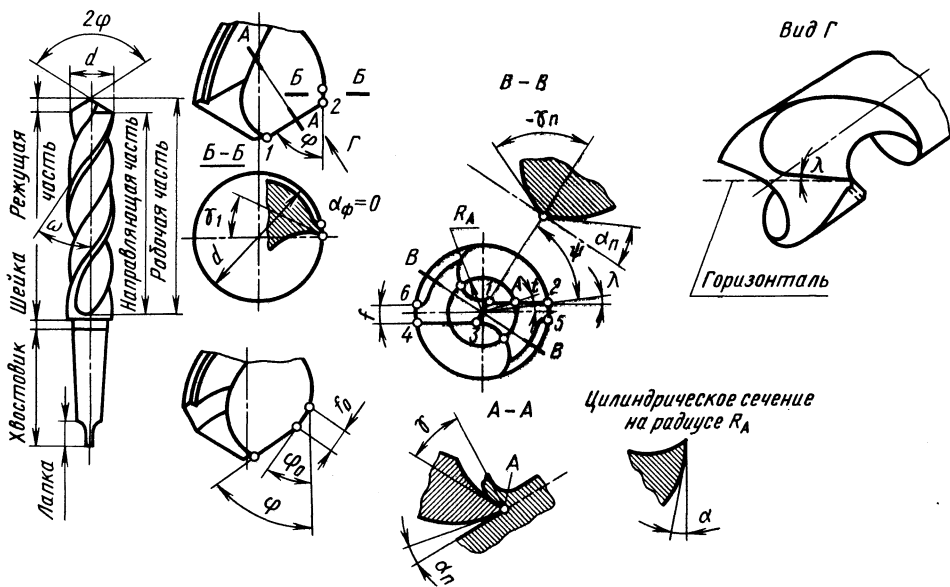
Конструкция спирального сверла с различной формой заточки
